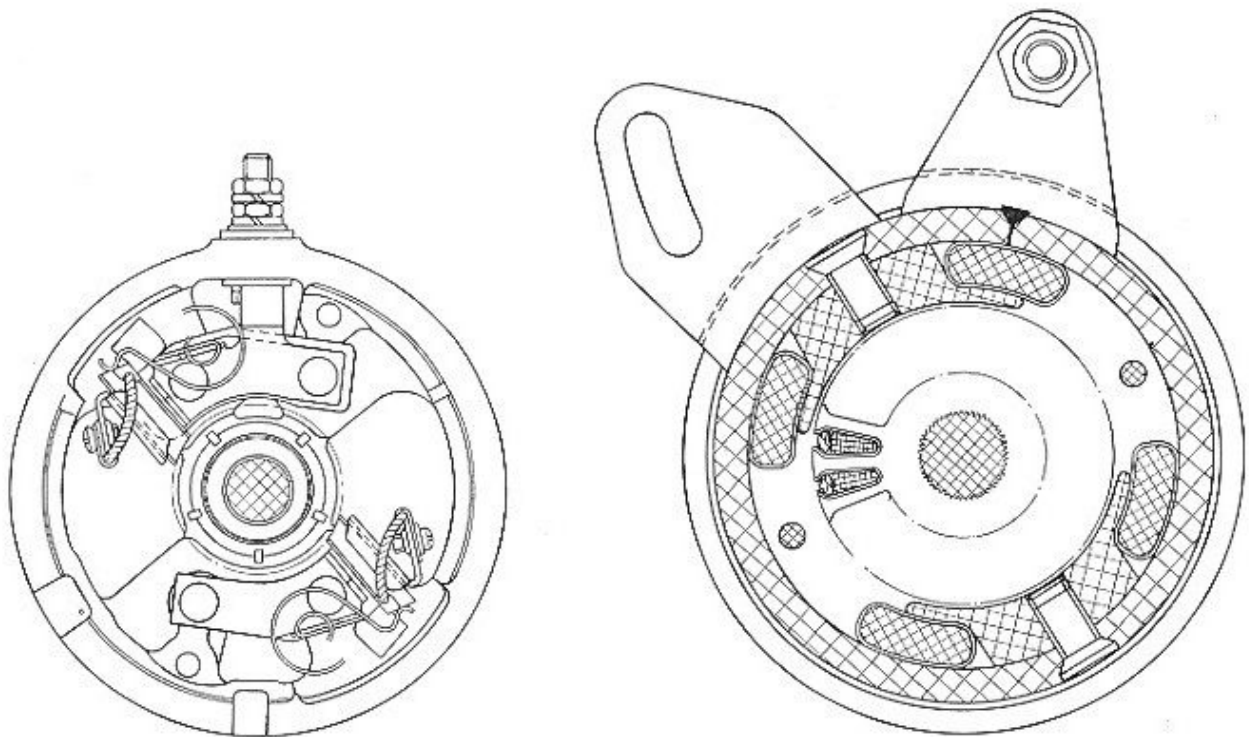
Querschnitt durch die Lichtmaschine und Ansicht des Kollektorlagers.
